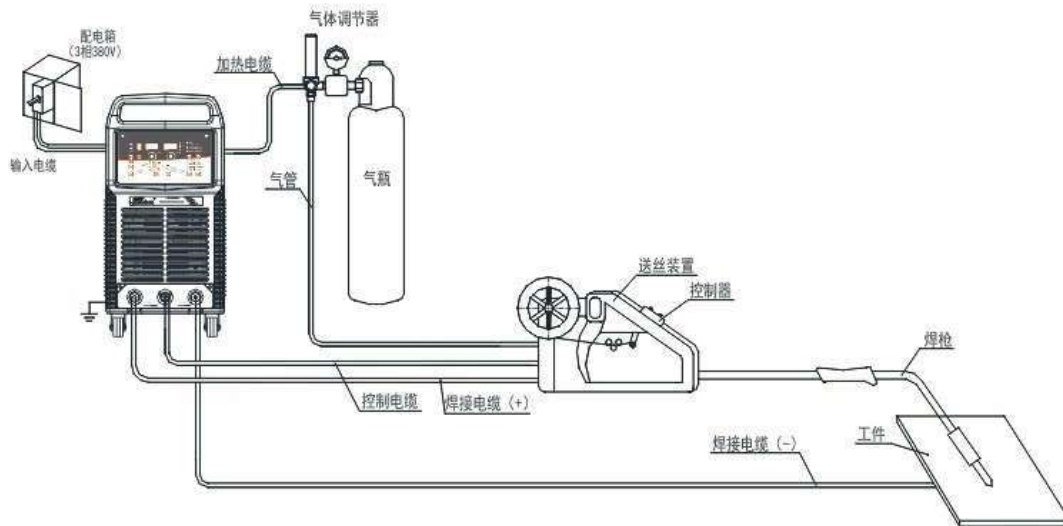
Принципиальная схема сварочного соединения в среде защитного газа.
